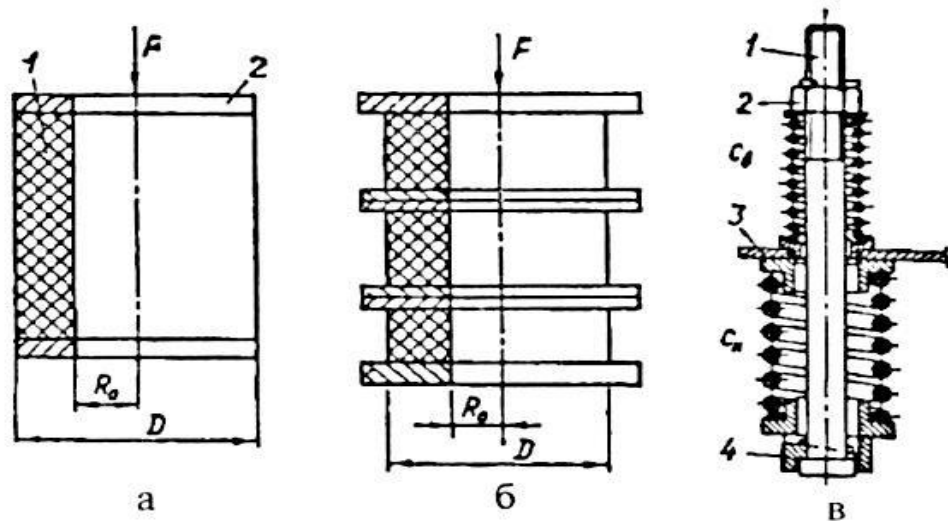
Конструкції пружних опор: а, б — гумометалеві; в — металеві
